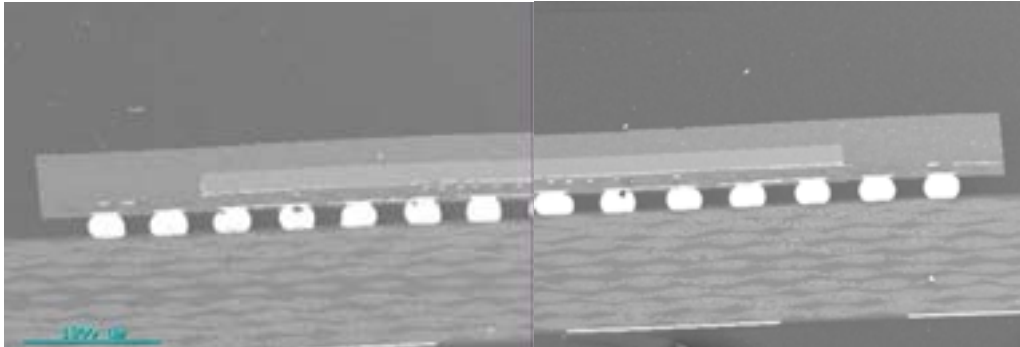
Boîtier BGA assemblé sur un circuit imprimé avant vieillissement
